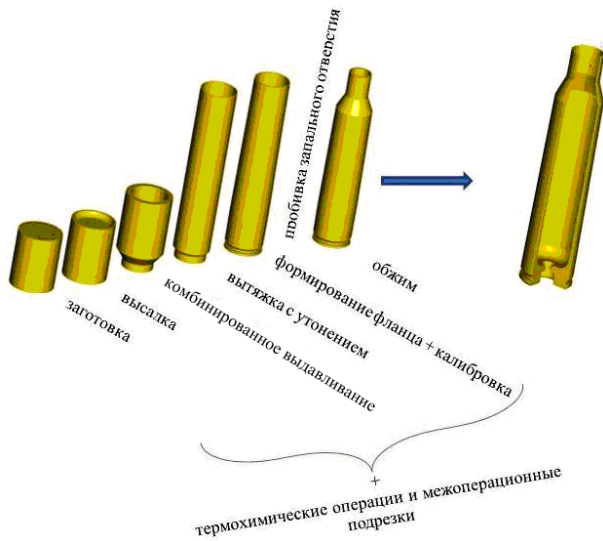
Маршрутная технологическая схема изготовления гильз к спортивно-охотничьим патронам с использованием прутковой заготовки
